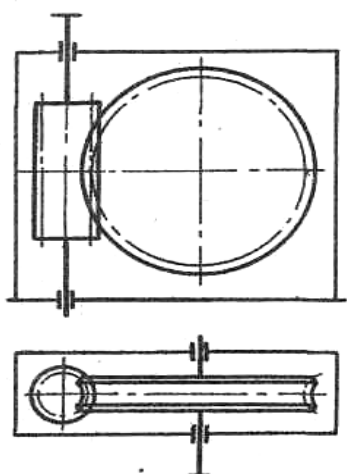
Схема червячного редуктора с вертикальным расположением червяка
